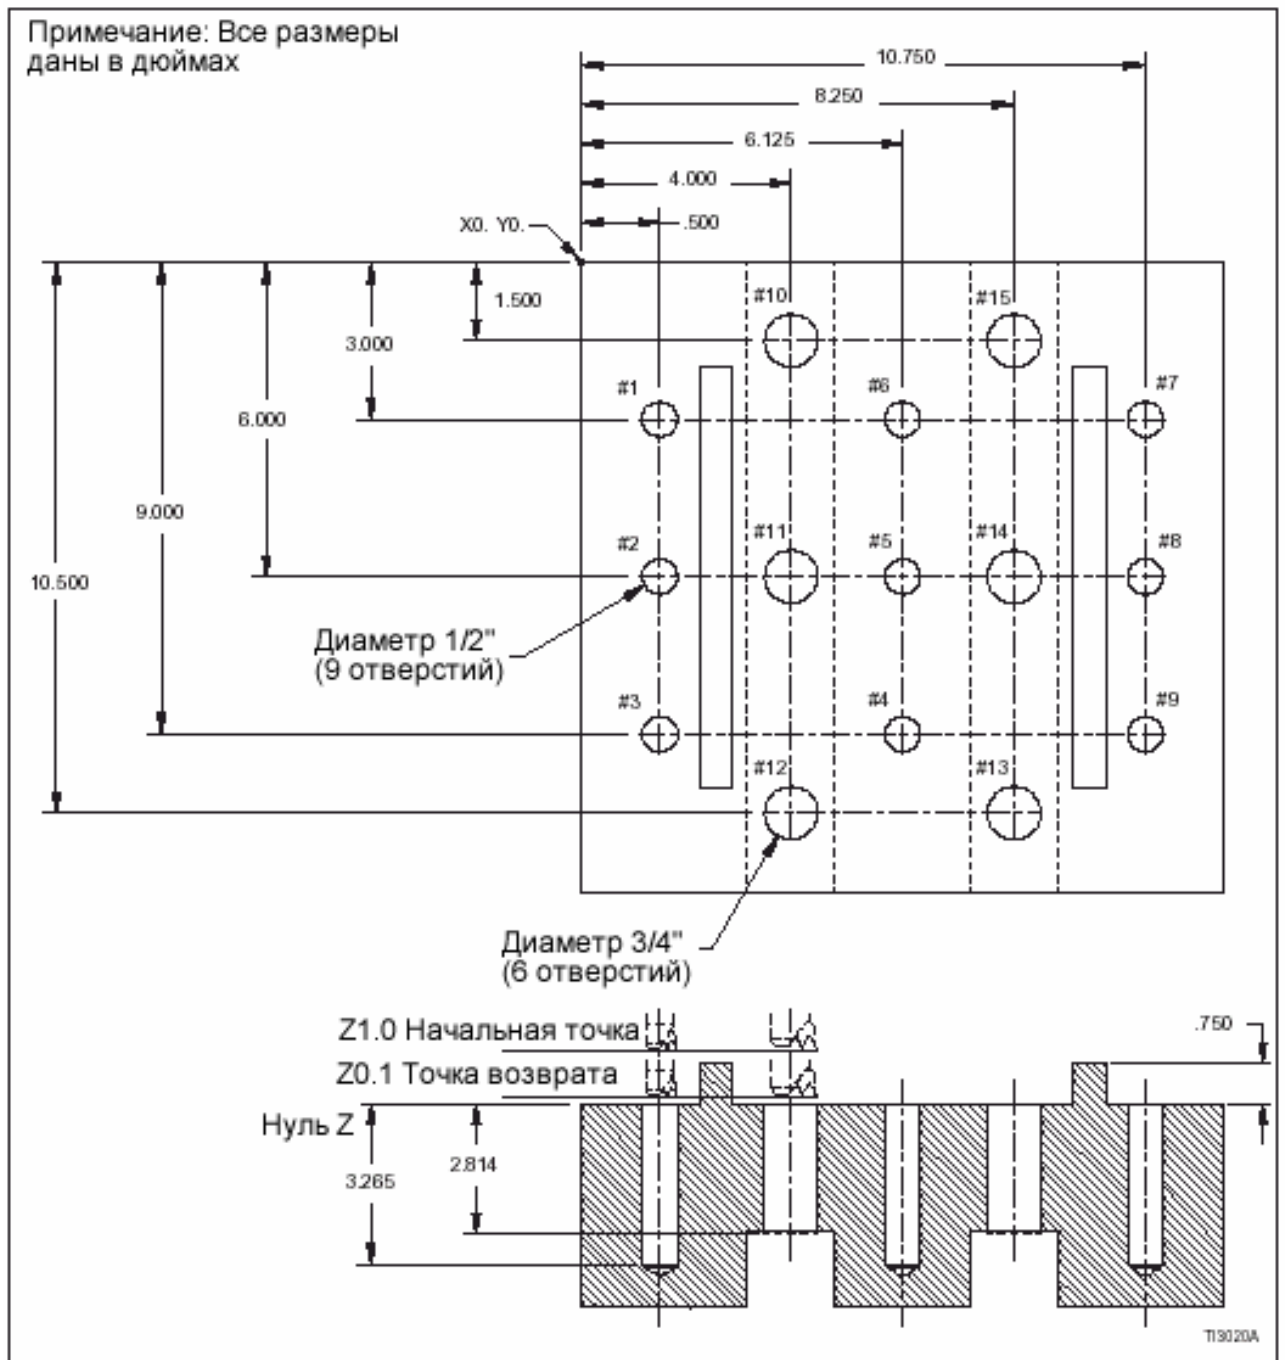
Типовая заготовка: Растачивание (рассверливание) нескольких отверстий
